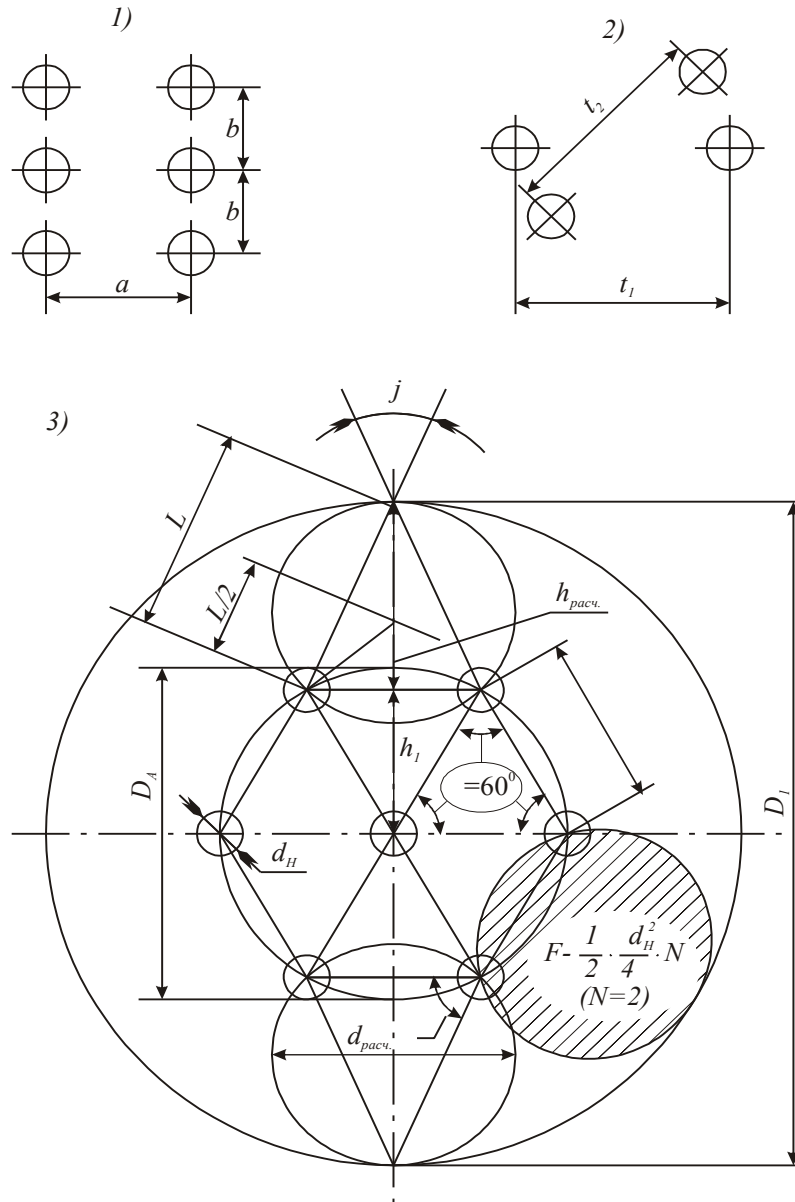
Схемы укПепления плоской стенки анкерными связями
